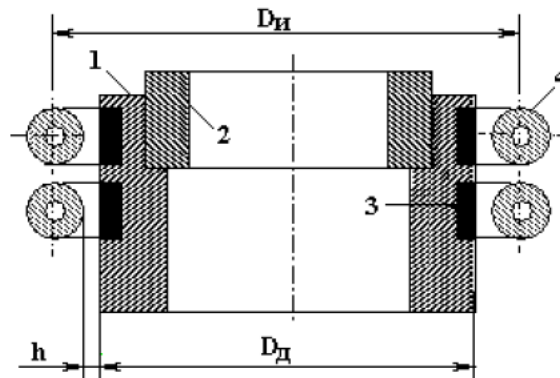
Схема нагрева при ВЧ пайке: 1, 2 – детали, 3 – зона нагрева, 4 – индуктор
